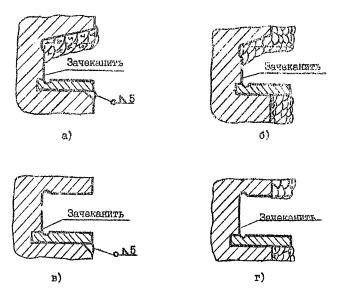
Схемы установки сменных вставок в канавки поршневых колец:
